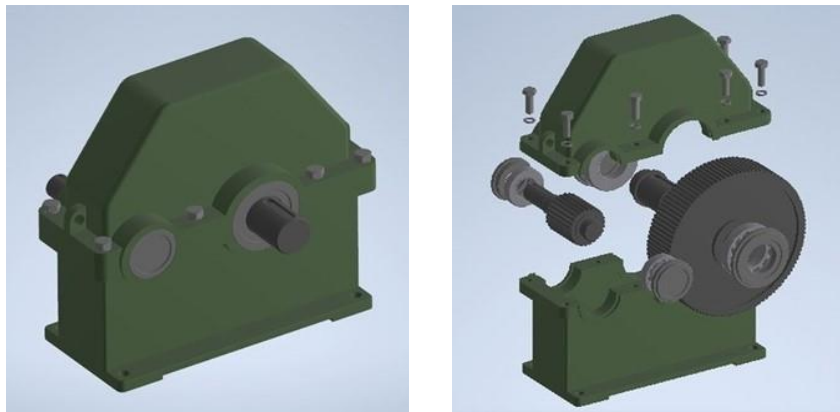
Фрагменты анимации разборки-сборки редуктора
